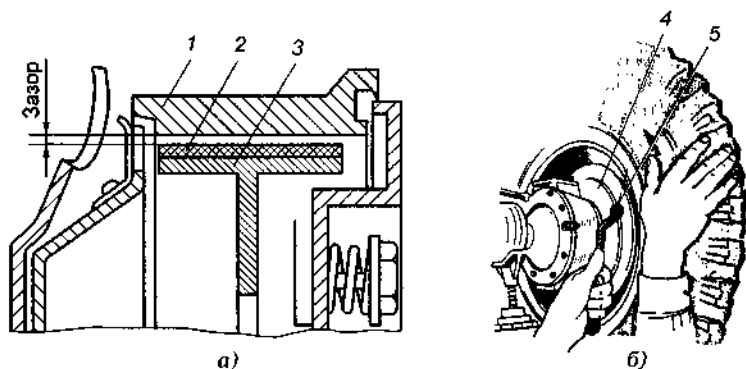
Проверка (а) и регулировка (б) зазора между тормозной колодкой и барабаном: 1 — барабан тормозного механизма; 2 — фрикционная накладка; 3 — тормозная колодка; 4 — опорный диск; 5 — регулировочный эксцентрик
